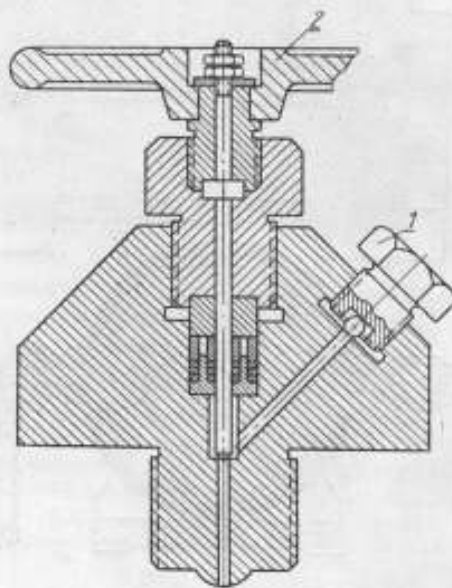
Устройство приспособления для нагружения рычага дополнительными грузиками под давлением
